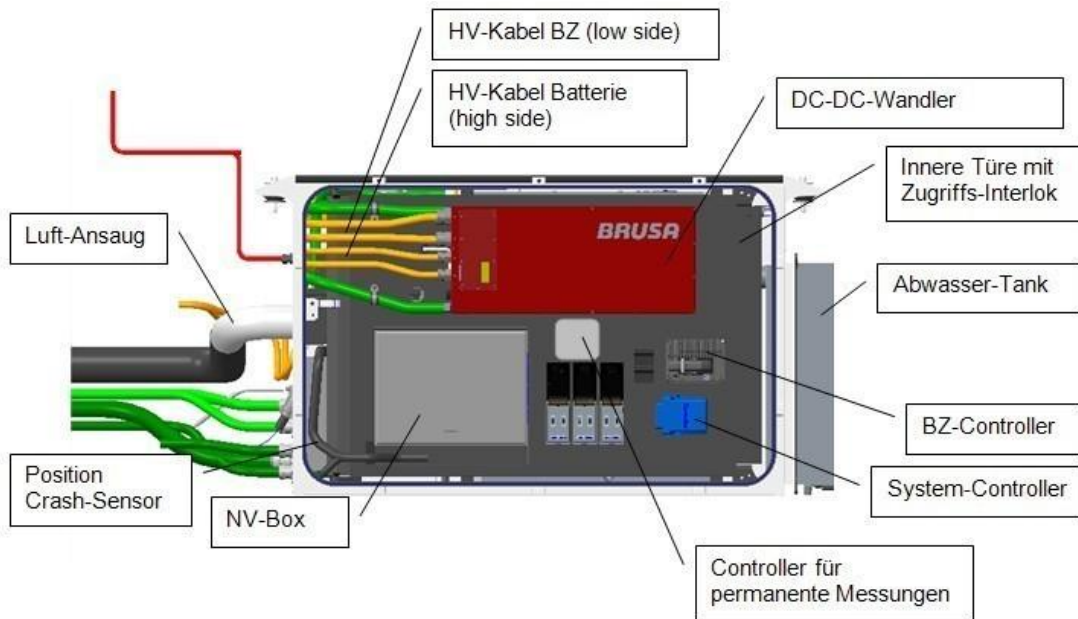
CAD-Seitenansicht der Brennstoffzellenbox mit geschlossener Schwenktüre
